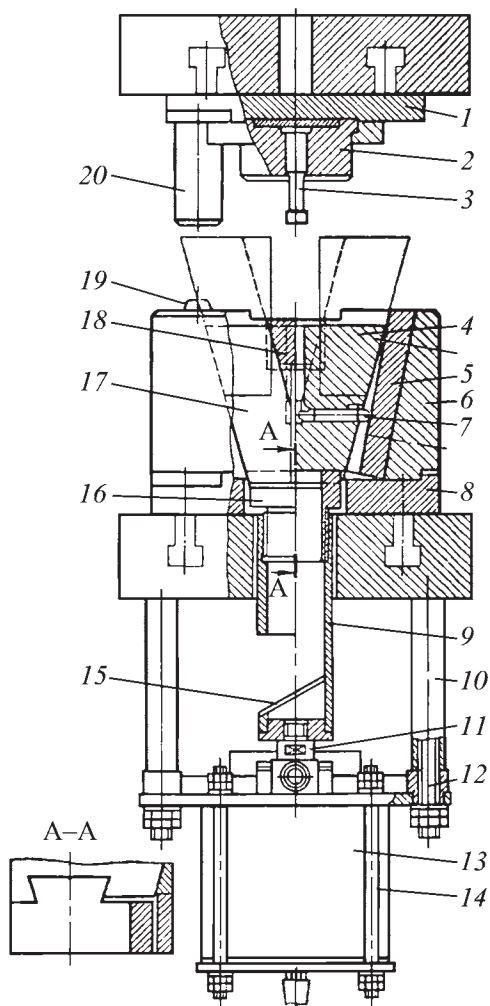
Блок штампа с разъемными матрицами и пневматическим устройством для раскрытия и закрытия матриц с выталкивателями поковок
